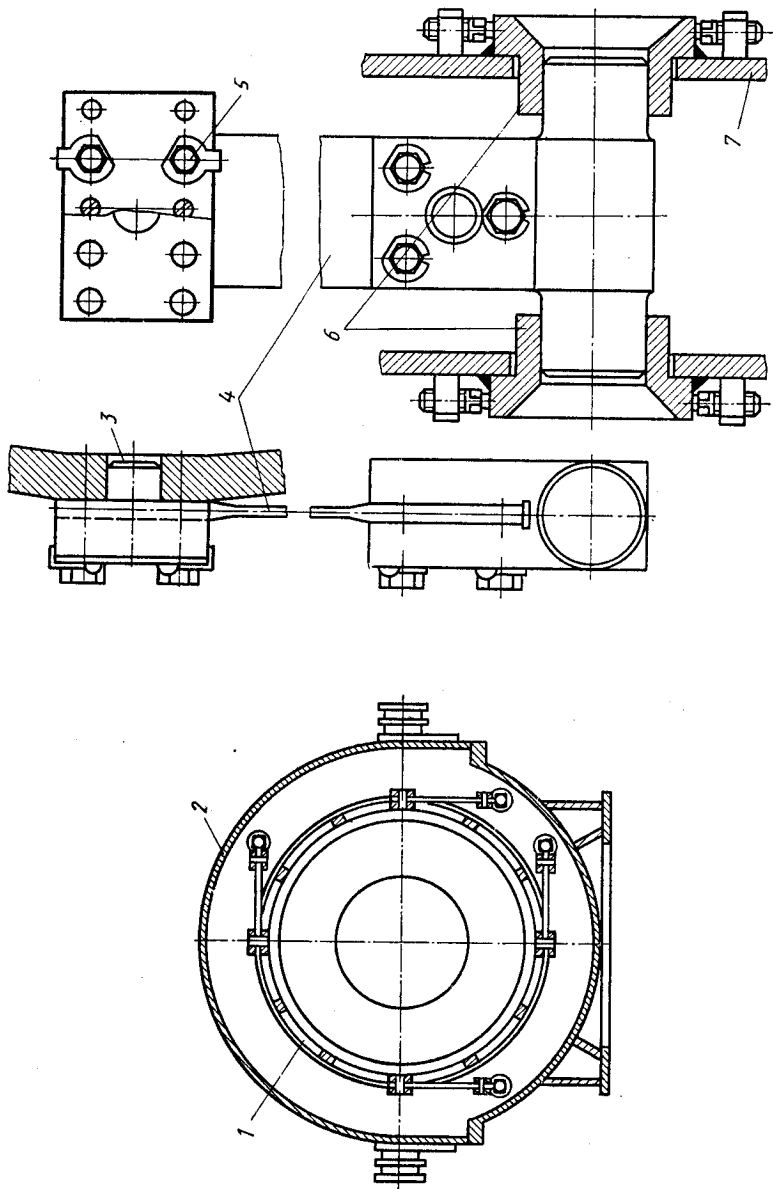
Подвеска сердечника статора в турбогенераторах серии ТГВ с двойным корпусом:
